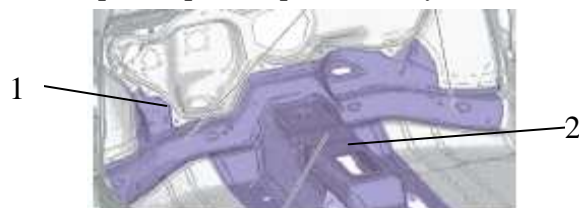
Нижняя передняя поперечина силового каркаса салона Volkswagen Passat B6 (вид снизу спереди):
